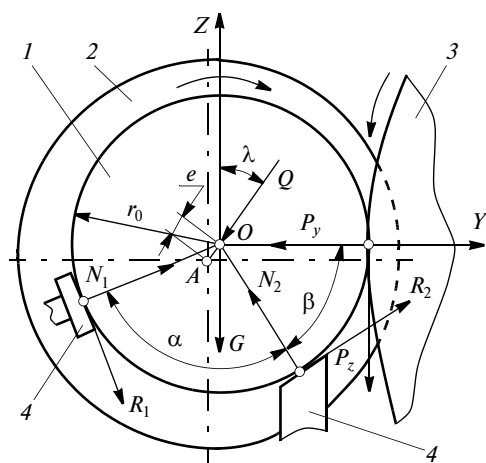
Схема действия сил при шлифовании на неподвижных опорах: *1* — заготовка; *2* — планшайба; *3* — шлифовальный круг; *4* — неподвижные опоры; α — угол между неподвижными опорами; λ — угол приложения силы *Q* прижима заготовки; P_y и P_z — радиальная и касательная составляющие силы резания; N_1 и N_2 — нормальные силы реакций опор; R_1 и R_2 — силы трения в местах контакта заготовки с опорами; r_0 — радиус заготовки
